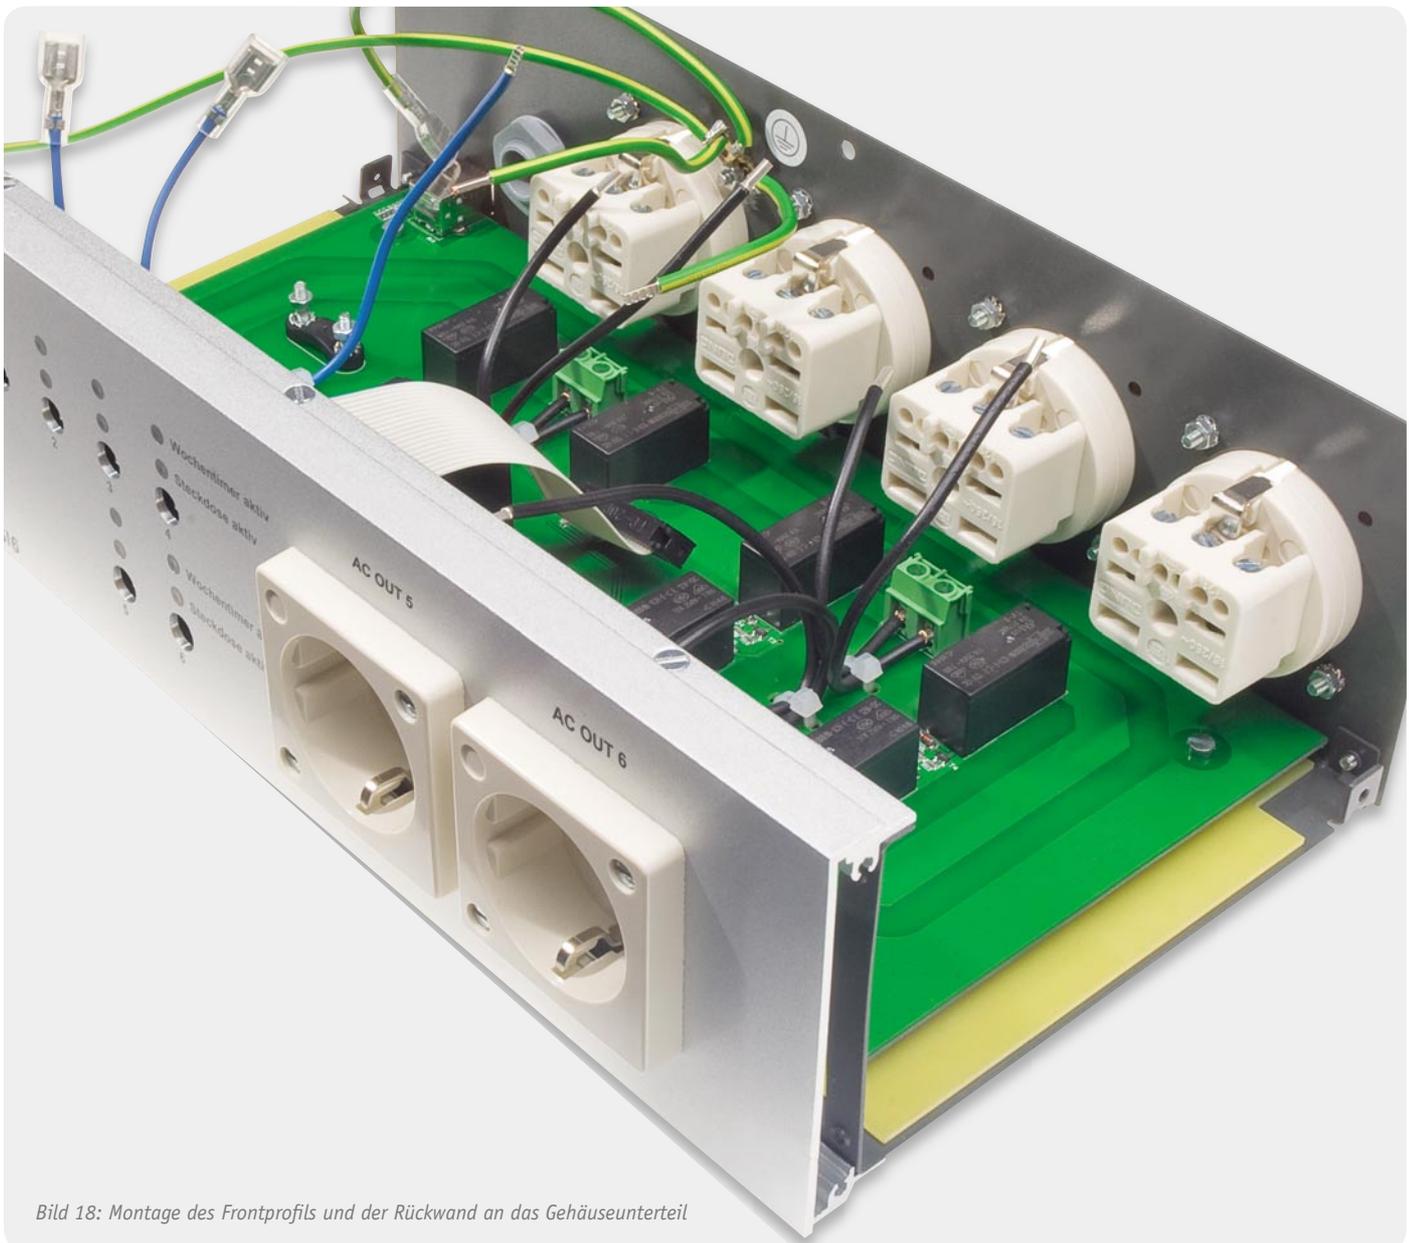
Montage des Frontprofils und der Rückwand an das Gehäuseunterteil
